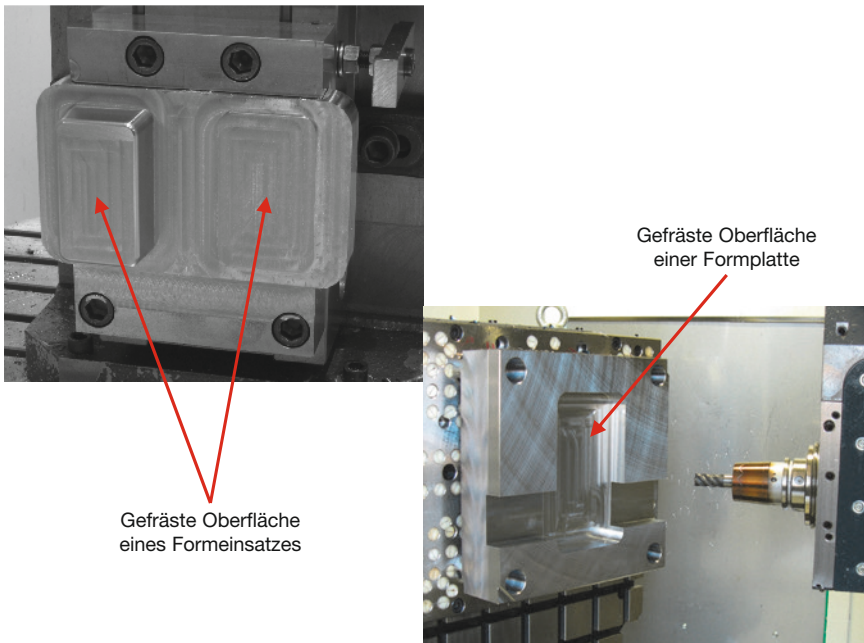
Gefräste Oberfläche [Werkbilder: Gebr. Heller GmbH, Nürtingen]
